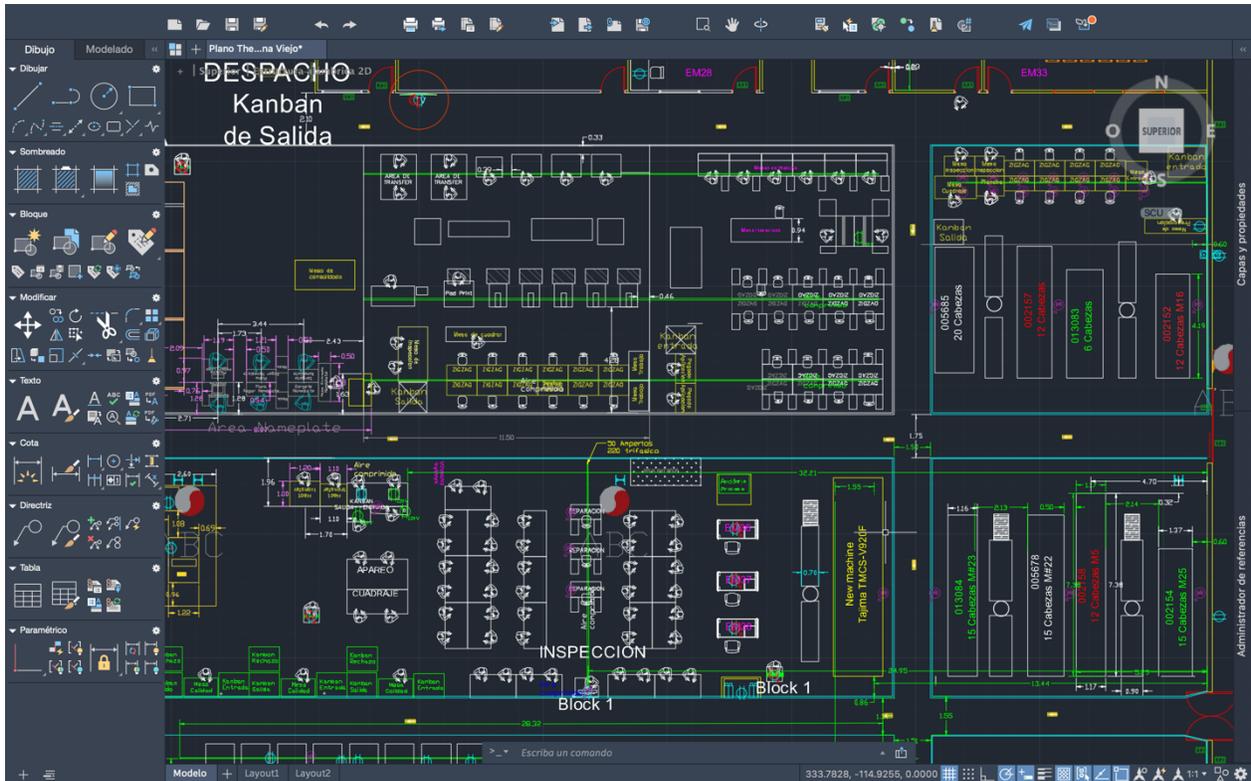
Plano viejo The arena (Fuente: Ingenieria Tegra)
